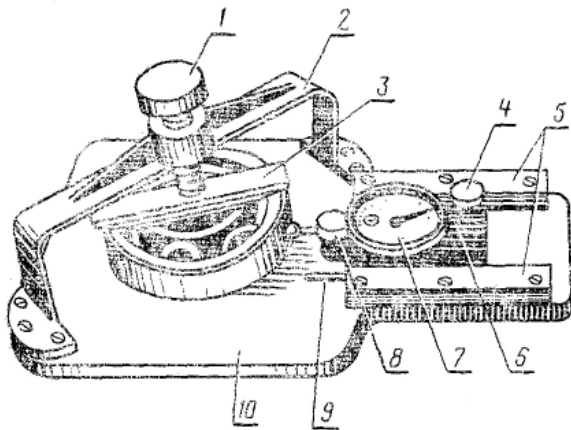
Прилад для вимірювання радіального биття зовнішнього кільця циліндрового підшипника обертання: 1 – настановний гвинт; 2 – міст; 3 – фіксатор внутрішнього кільця; 4 – гвинтовий затиск; 5 – направляючі; 6 – каретка; 7–індикатор; 8 – гвинт; 9 – паз; 10 – плита.
